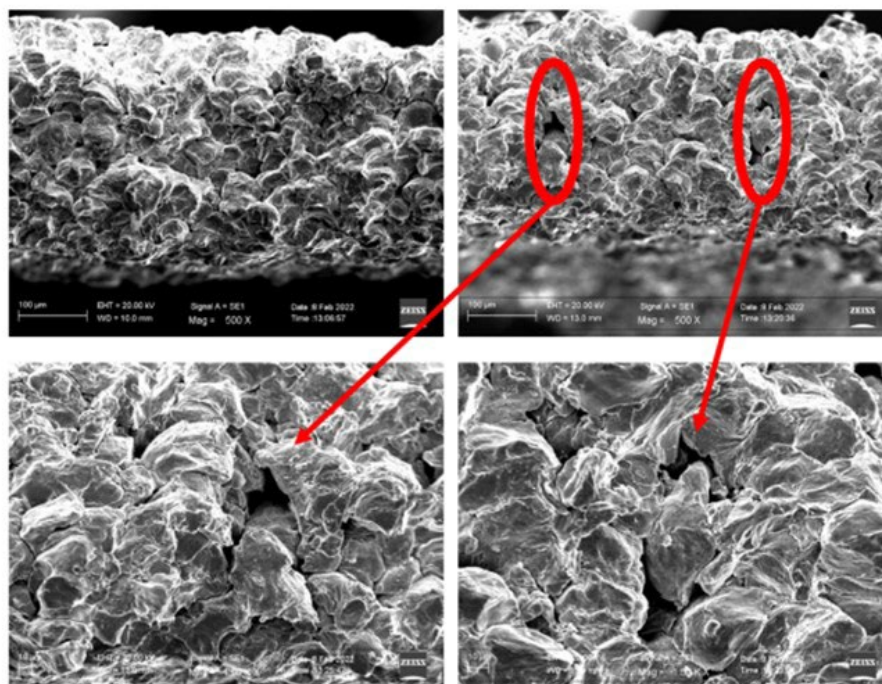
Superficie di frattura dei campioni testati in flessione ciclica alla corsa massima di 1,5 mm (a) e 2 mm (b) / Fracture surface of the samples tested in cyclic bending at the maximum stroke of 1.5 mm (a) and 2 mm (b).
